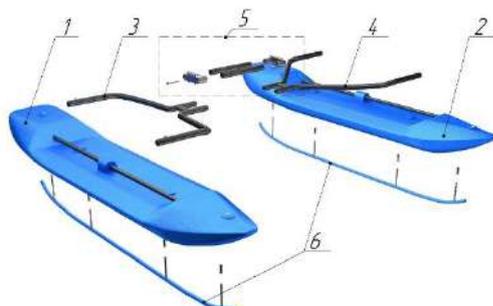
«Взрыв-схема» универсального приспособления к снегоходу:
